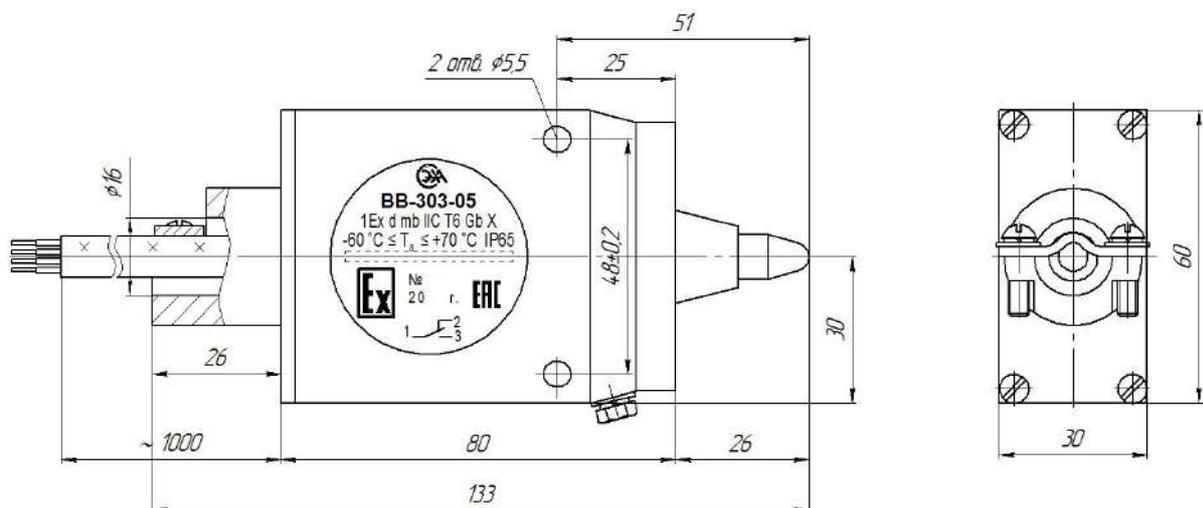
Габаритные и установочные размеры выключателей BB-303-03...BB-303-05
